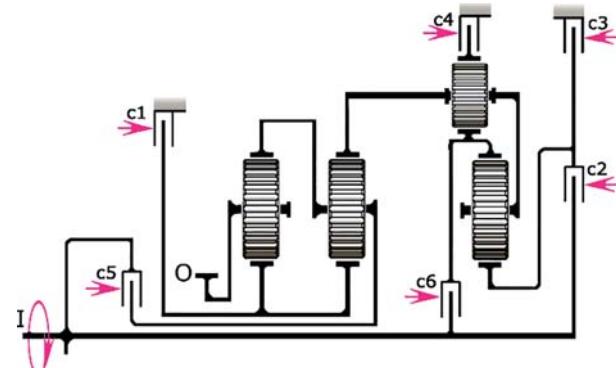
Кинематическая схема 9-ти ступенчатой планетарной коробки передач фирмы ZF Friedrichshafen:
